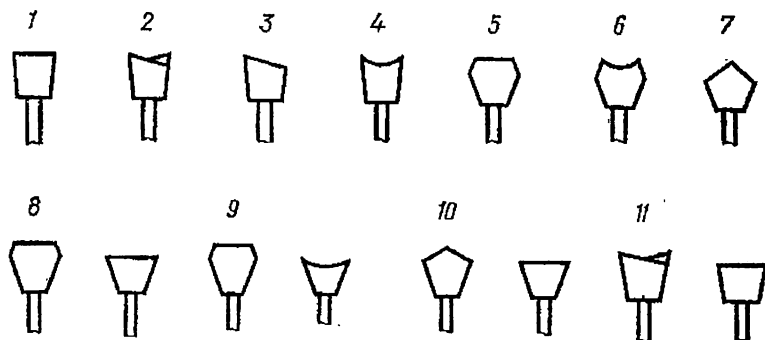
Формы зубьев пил с твердосплавными пластинками:
